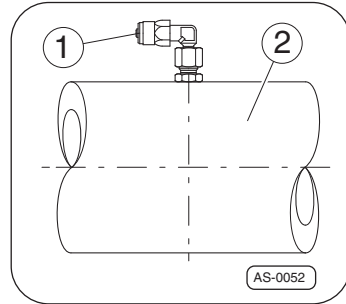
· Coude d'assemblage sur le tube d'essieu
